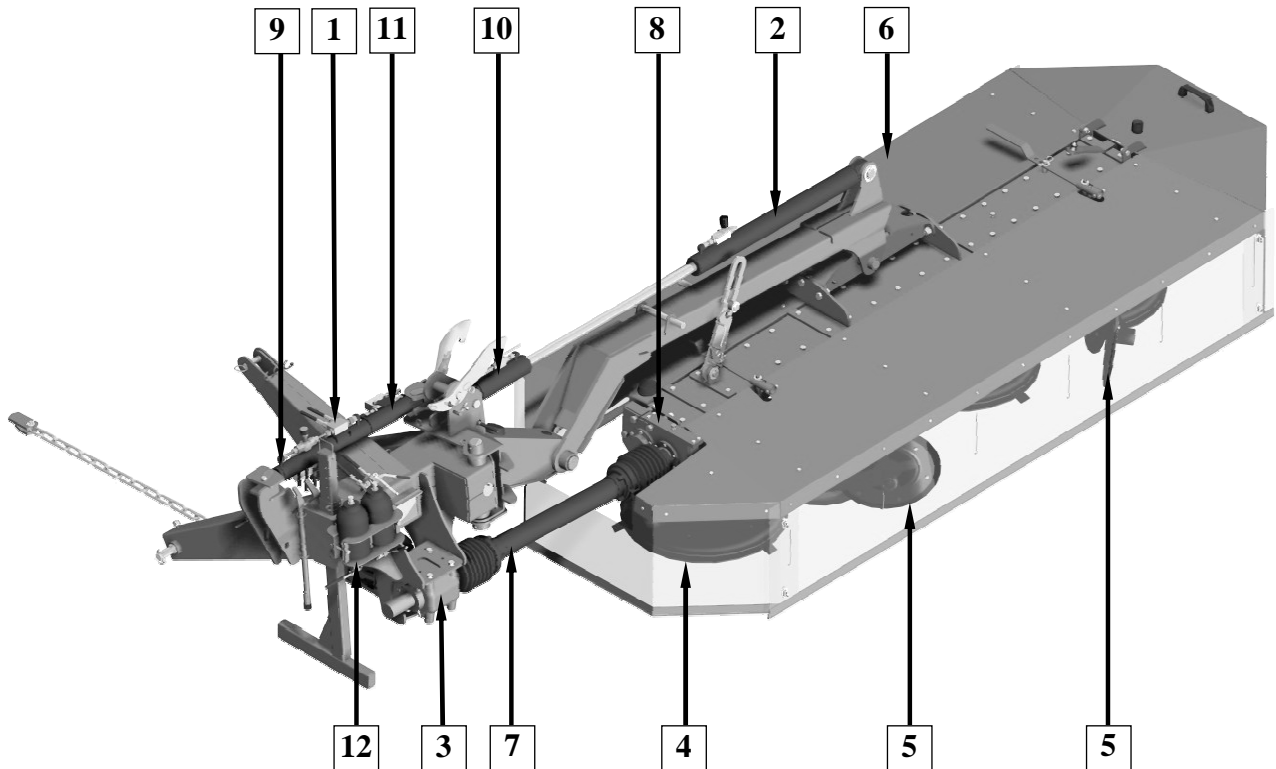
Gesamtansicht eines Heck-4-Trommelmähers mit Mittenaufhängung
